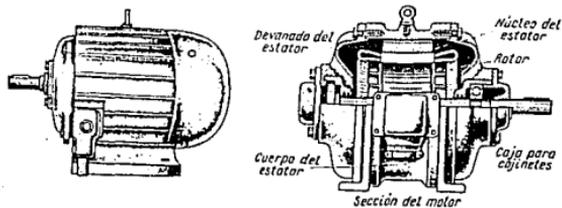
Aspecto general y corte de un motor asincrónico con rotor de jaula de ardilla
